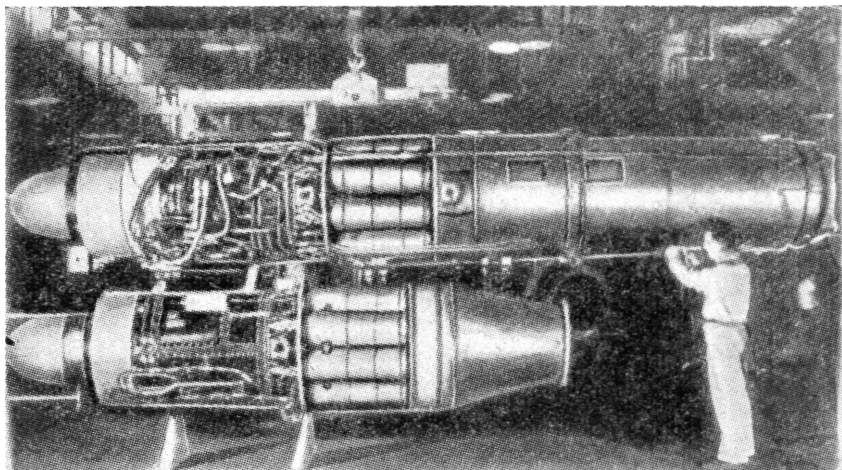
Двигатель с форсажной камерой (вверху) и без нее.
